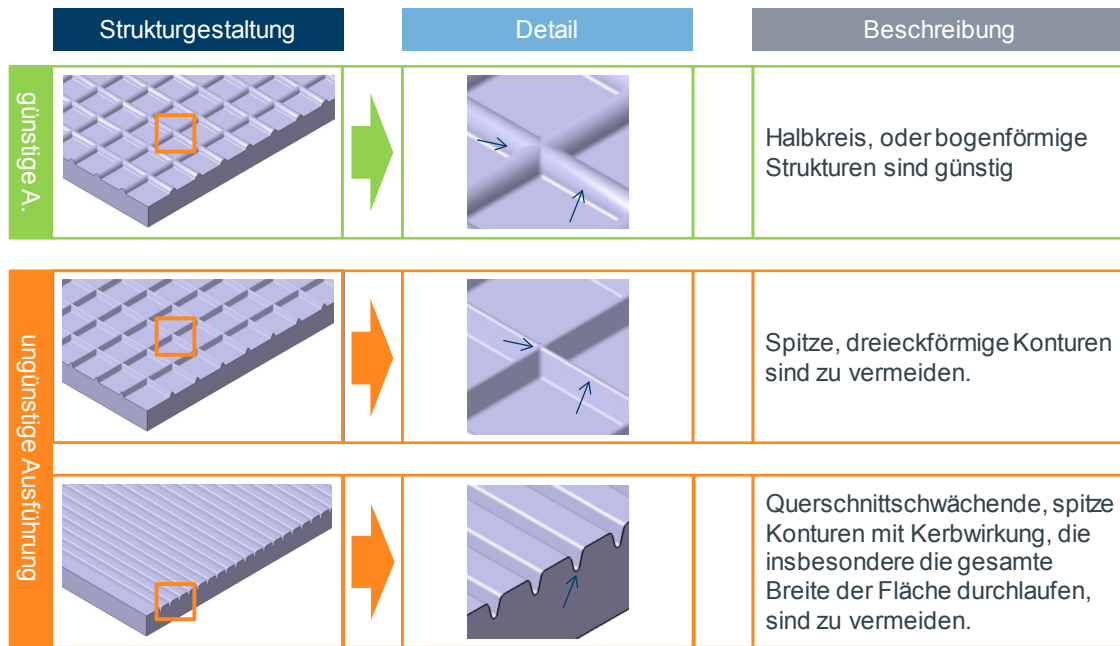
Konstruktionsrichtlinie – Vergleich günstiger und ungünstiger Ausführung der Oberflächenstrukturierung, Darstellung des Bauteils
